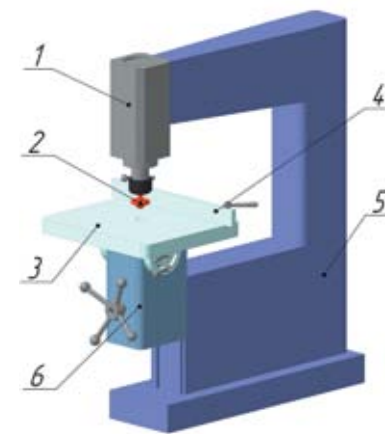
Фрезерный станок с верхним расположением шпинделя: 1 – фрезерный модуль, 2 – фреза, 3 – стол, 4 – линейка съемная, 5 – станина, 6 – механизм вертикального перемещения и наклона стола
